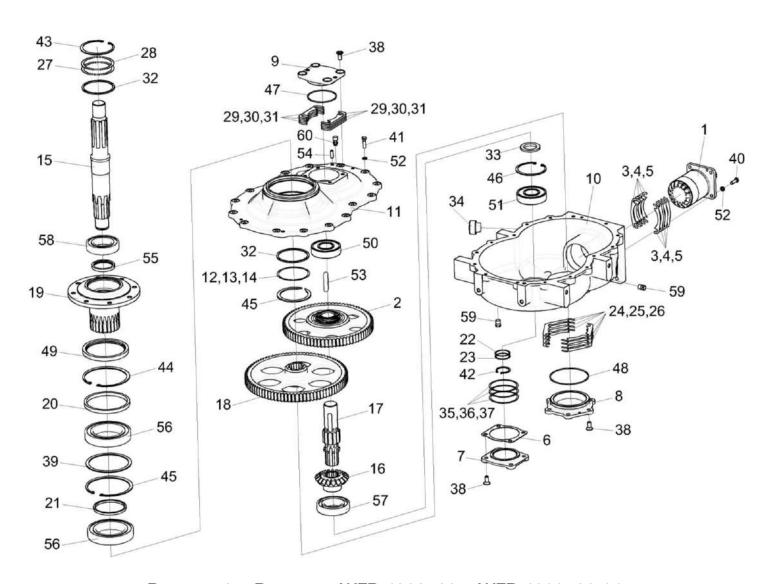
Редуктор ЖГР 4803500 и ЖГР 4803500-01
